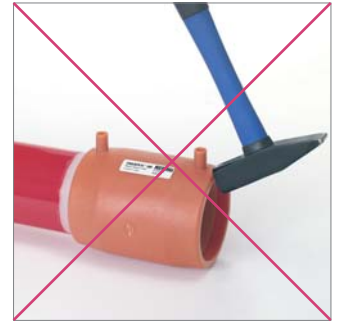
Sollte die Elektroschweißmuffe FUSAPEX nicht von Hand aufsteckbar sein, nie mit Eisenhammer sondern mit geeigneten Mitteln auftreiben.
